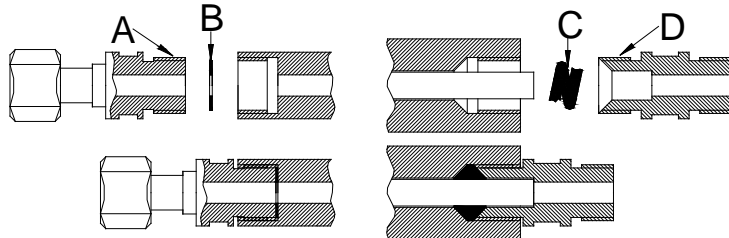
Aufbau Absaugrohre mit festem Innenrohr.
